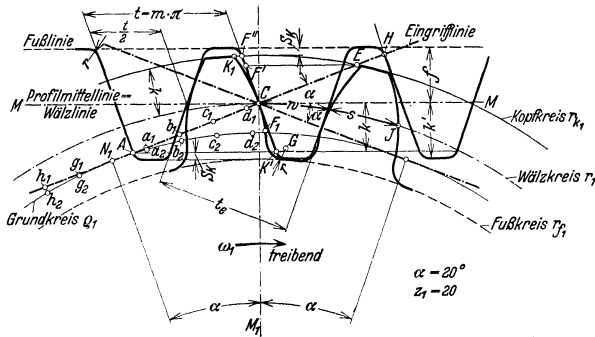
Zahnstange als erzeugendes Werkzeug.
